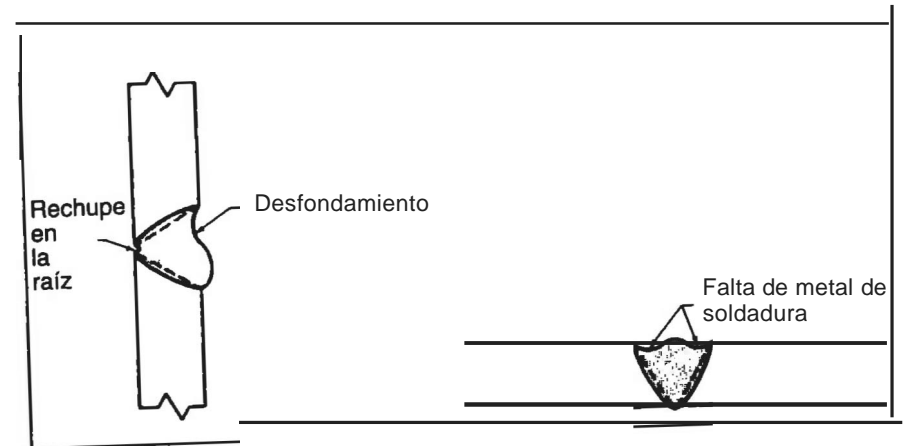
FALTA DE METAL DE SOLDADURA
